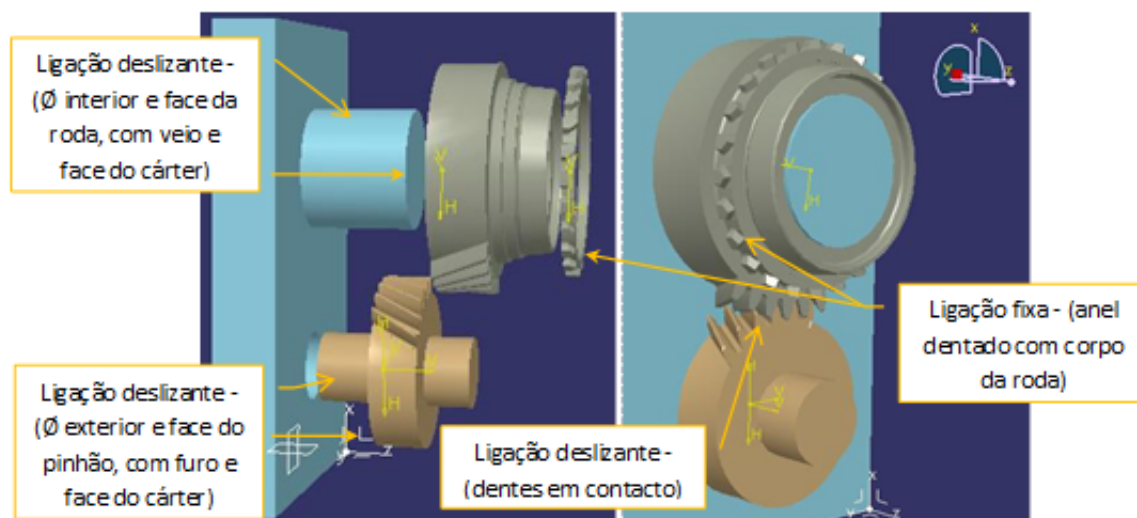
Ligações entre os componentes - engrenagem de denteado helicoidal
